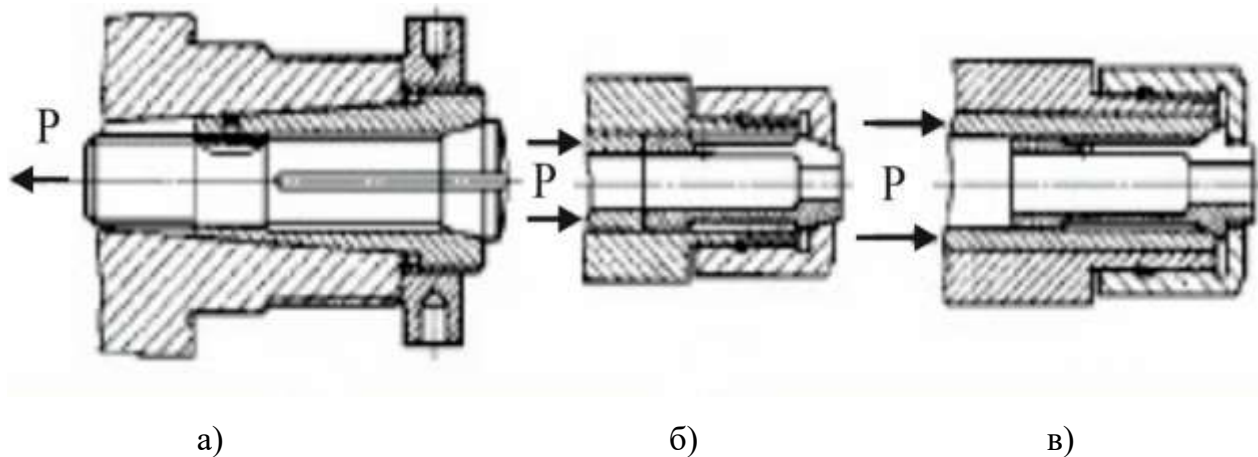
Схеми затискання заготовки у цангових патронах.
